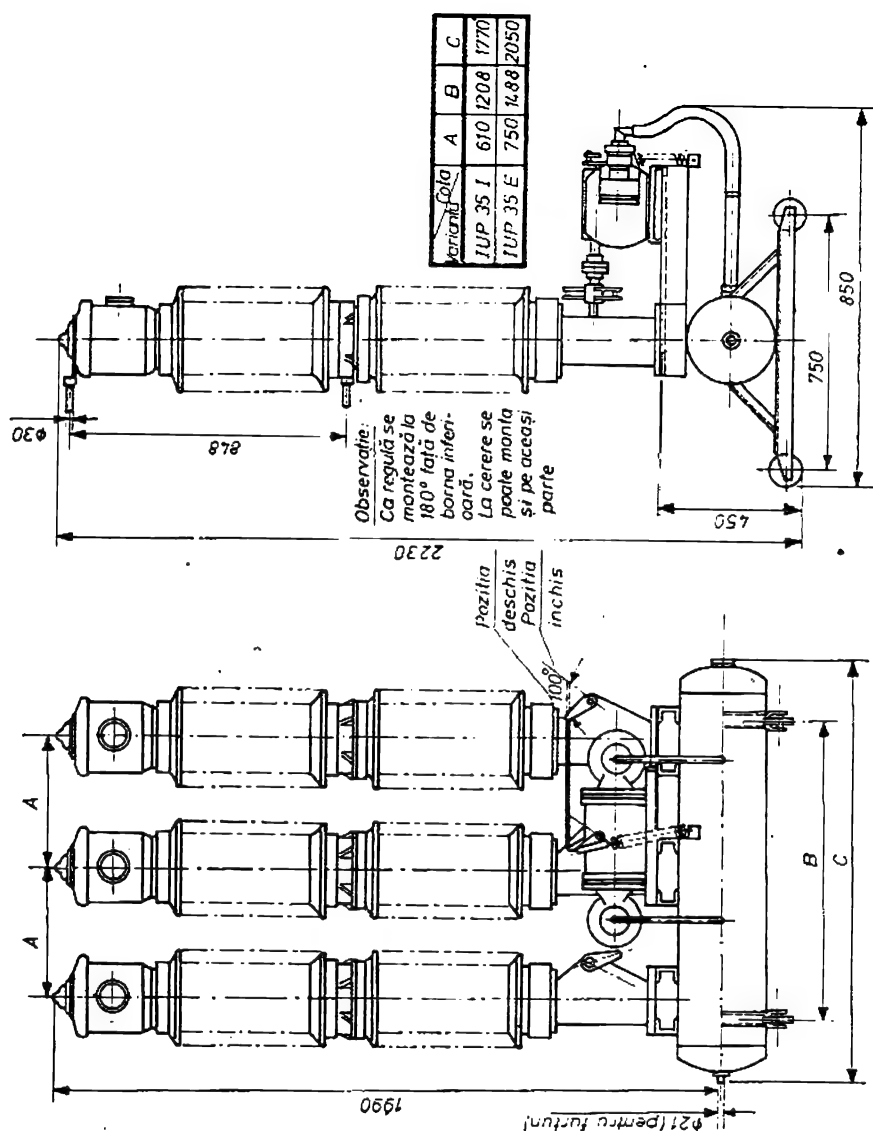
Înteruptoare IUP—35/1250 I, E cu acționare pneumatică. Dimensiuni de gabarit.
